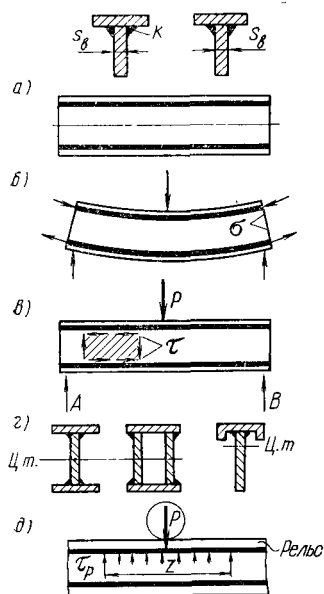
К расчету поясных швов сварных балок:
